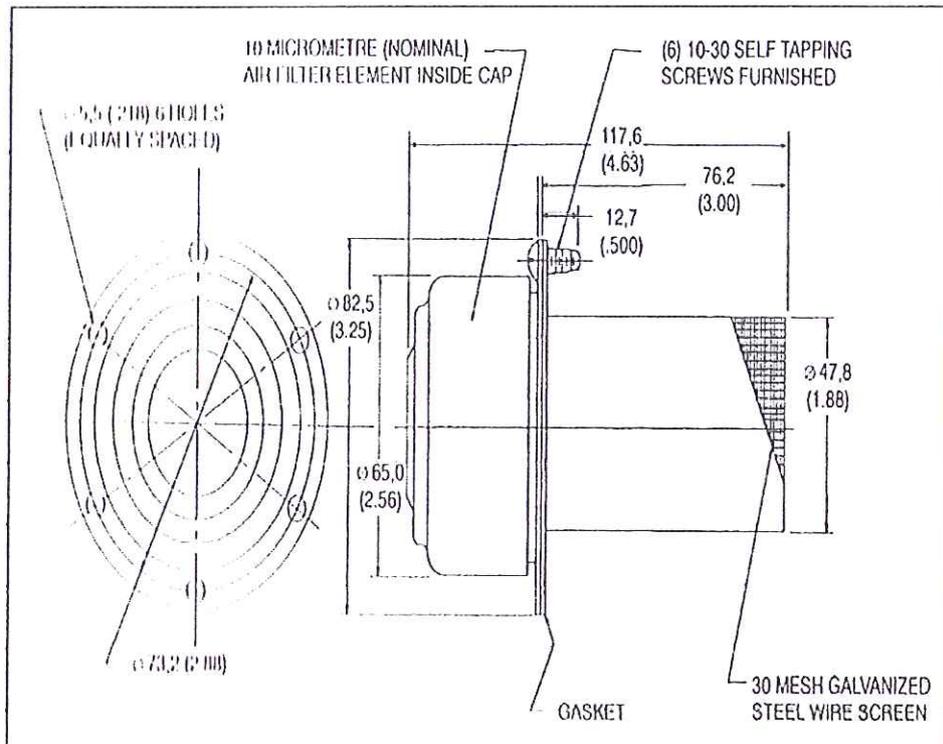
TAPÓN DE LLENADO DEL TANQUE [6]
